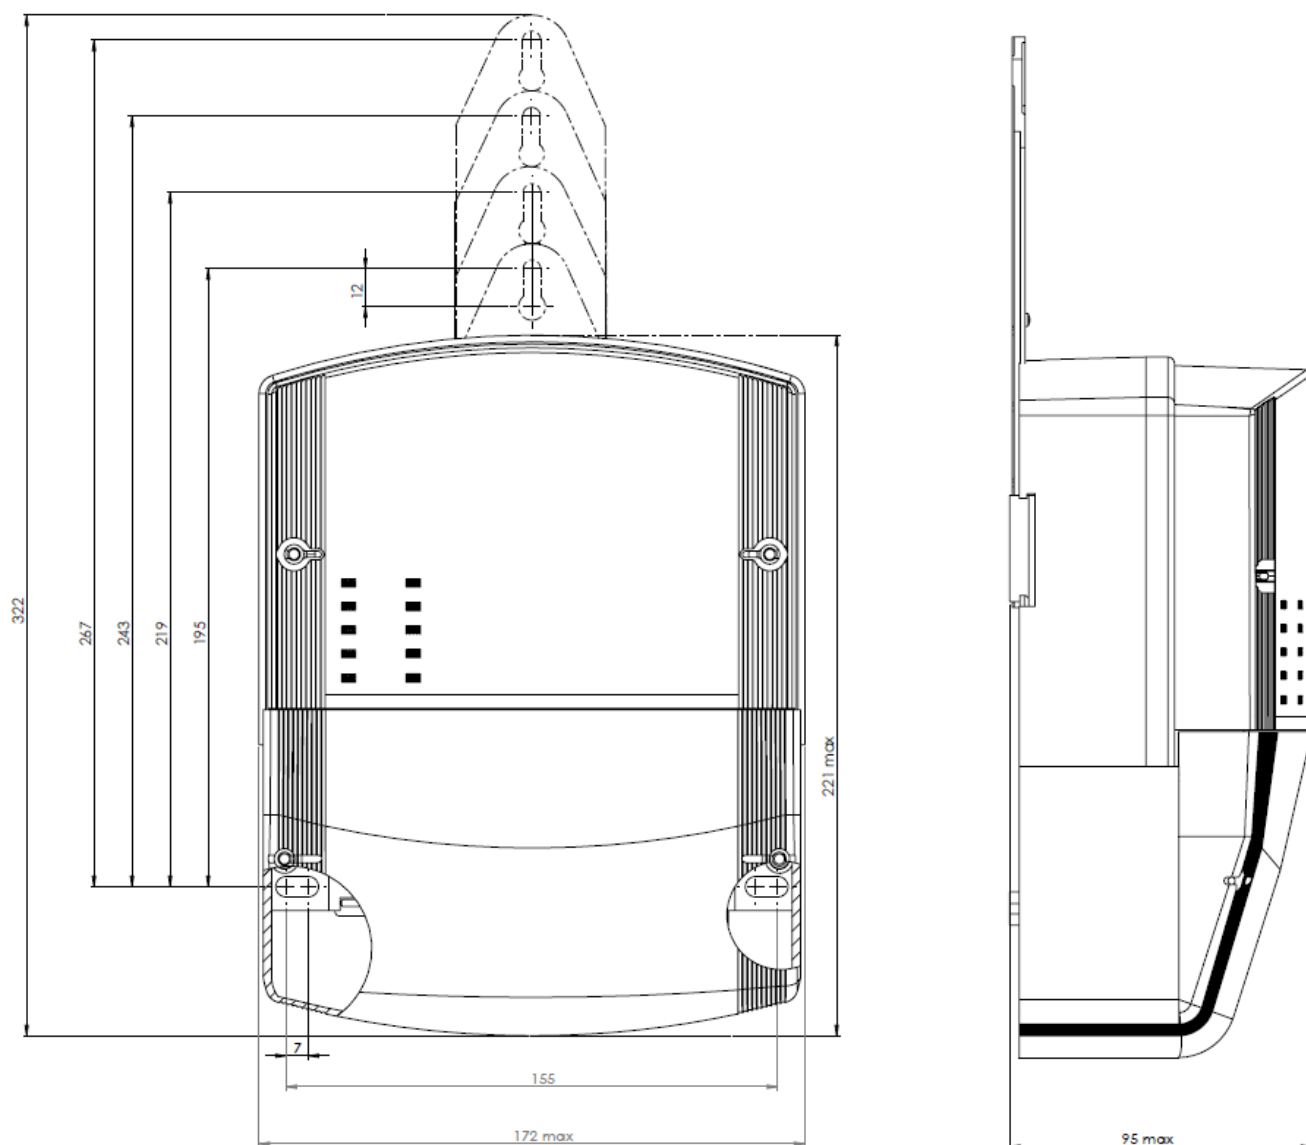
Габаритные и установочные размеры счетчиков
